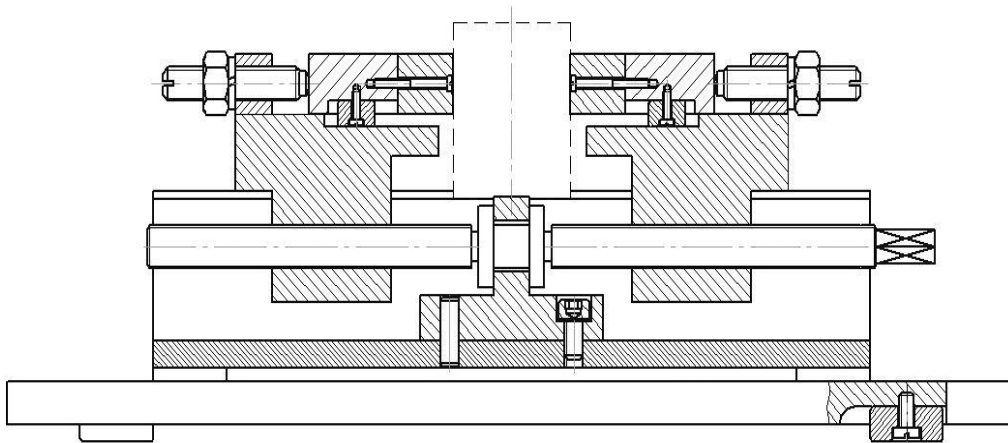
Схема верстатного пристрою для закріплення заготовки
